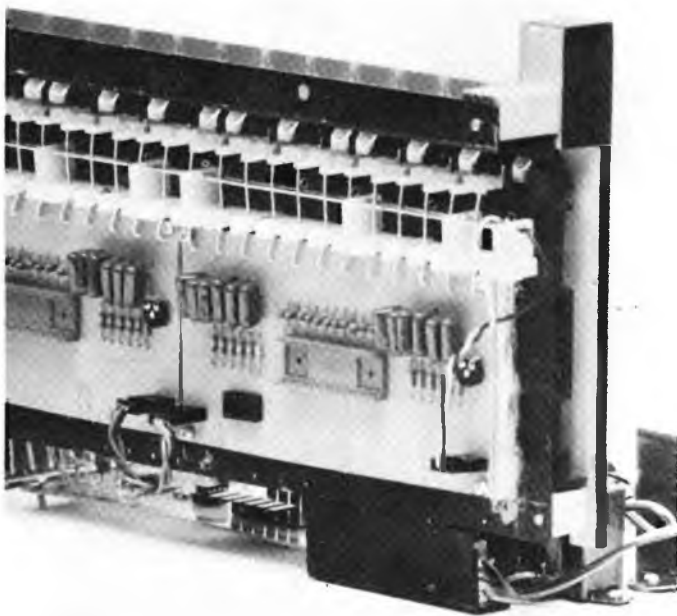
In questa foto il lettore può prendere visione del particolare del collegamento alle barre di contatto. La barra superiore, come viene evidenziato dalla foto, è collegata al -27 V, mentre la barra inferiore è collegata al VSS (GND).
